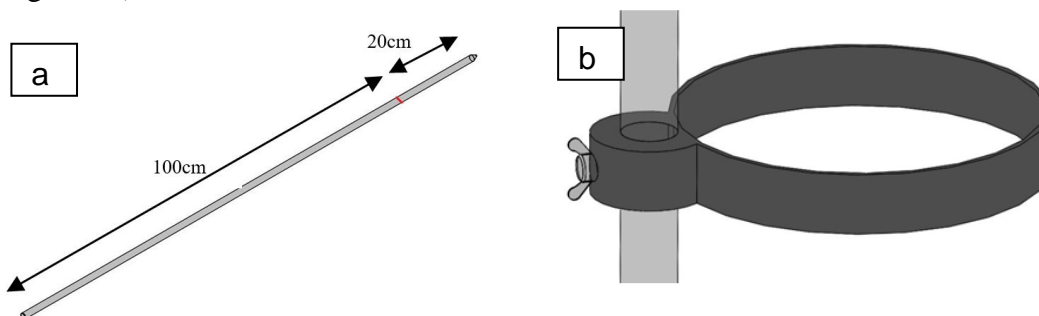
a) haste de sustentação, vista isométrica; b) Suporte com porca borboleta
